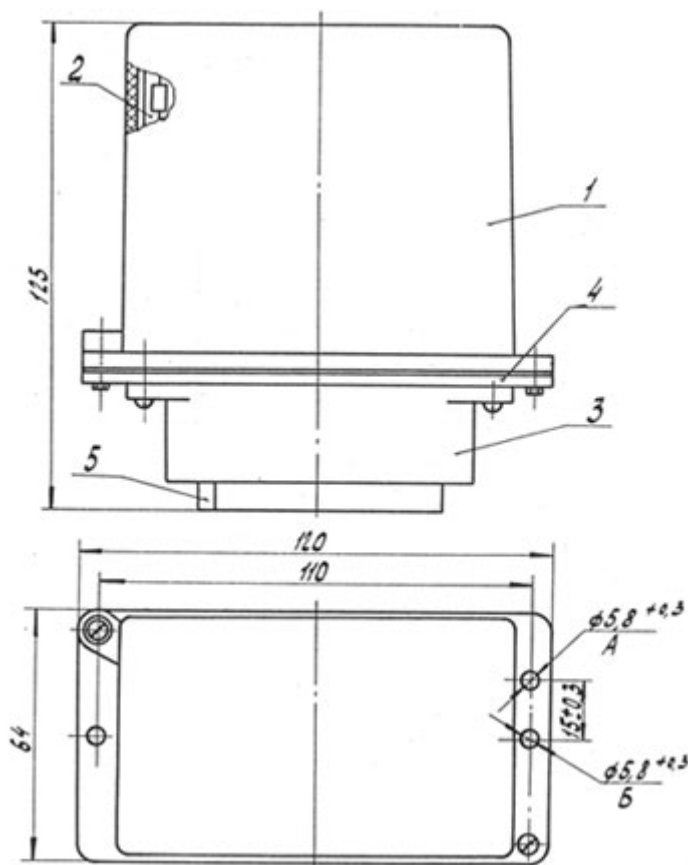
Габаритные и установочные размеры блоков БДУ-4-3
